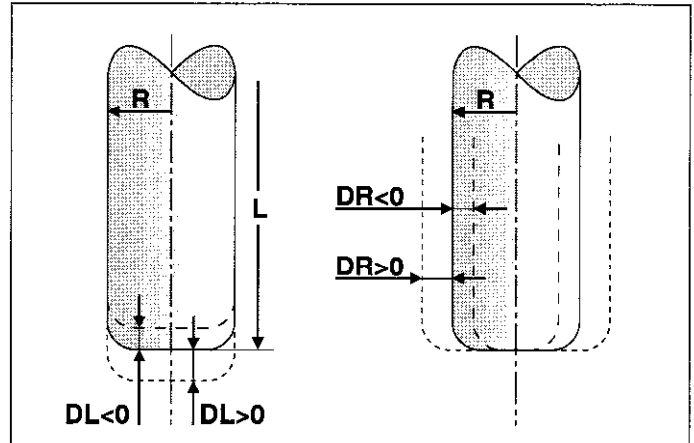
Aufmaße DL, DR beim Eckenradiusfräser
